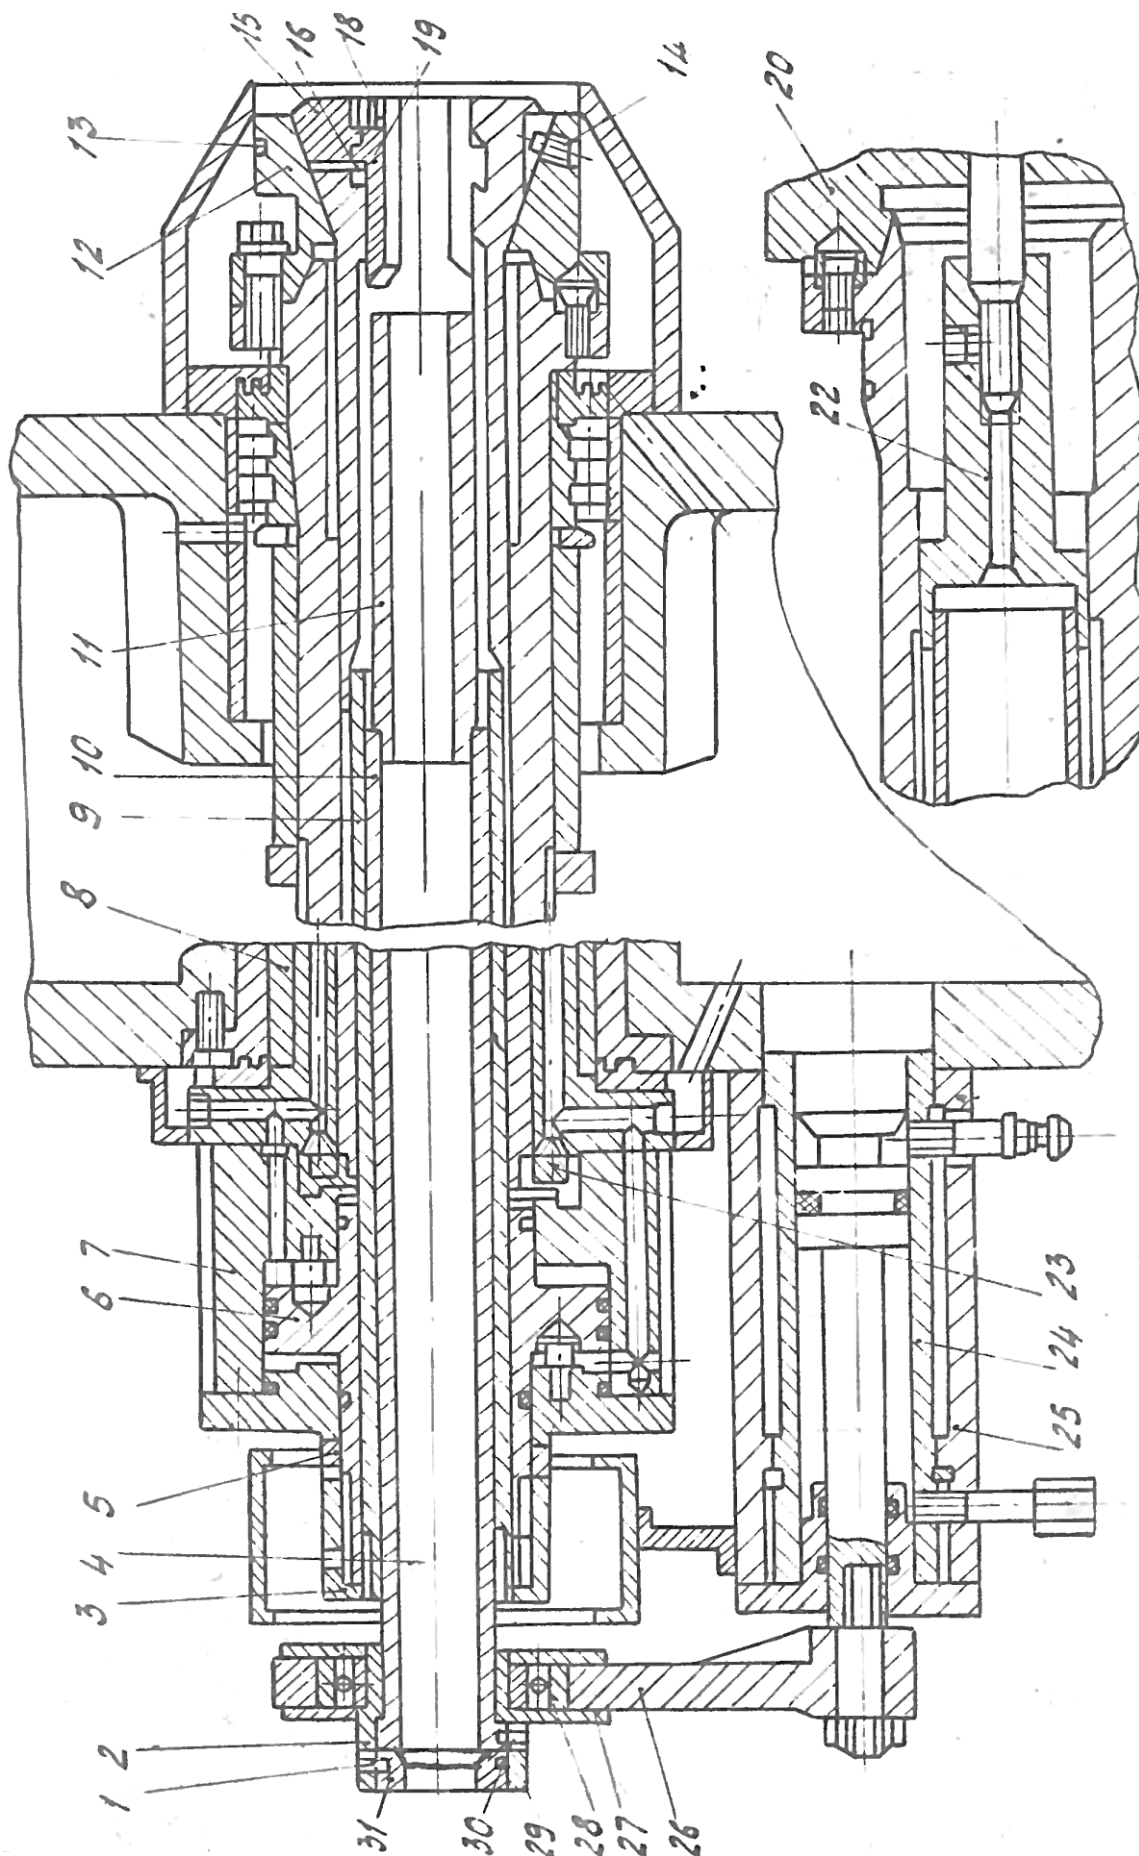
Механізм затиску та подачі матеріалу токарно-револьверного верстату з ЧПК мод. 1В340Ф30
